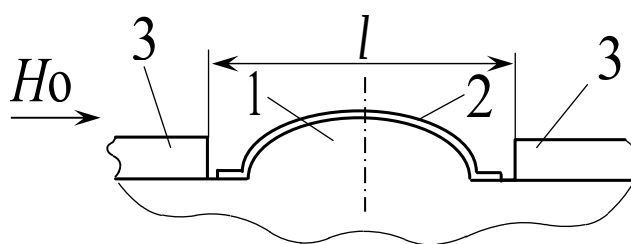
Вид и расположение КМИ при осуществлении способа магнитографического контроля [8]: 1 – контролируемый сварной шов; 2 – магнитная лента; 3 – концентраторы магнитной индукции
